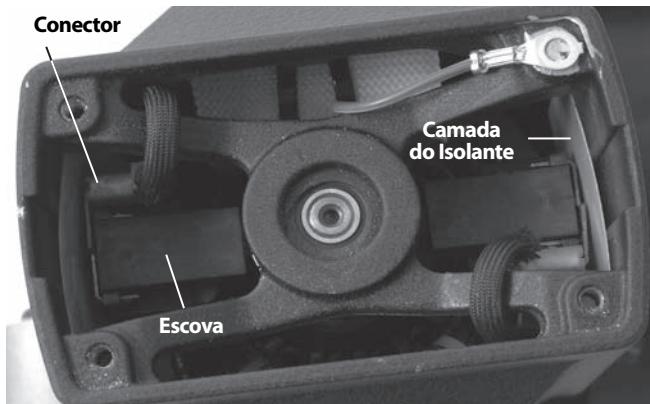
Colocação da Escova - Tampa do Motor Removida
